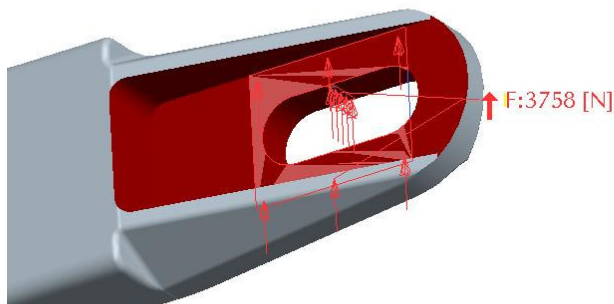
Definice otočného uložení zadní kyvné vidlice
